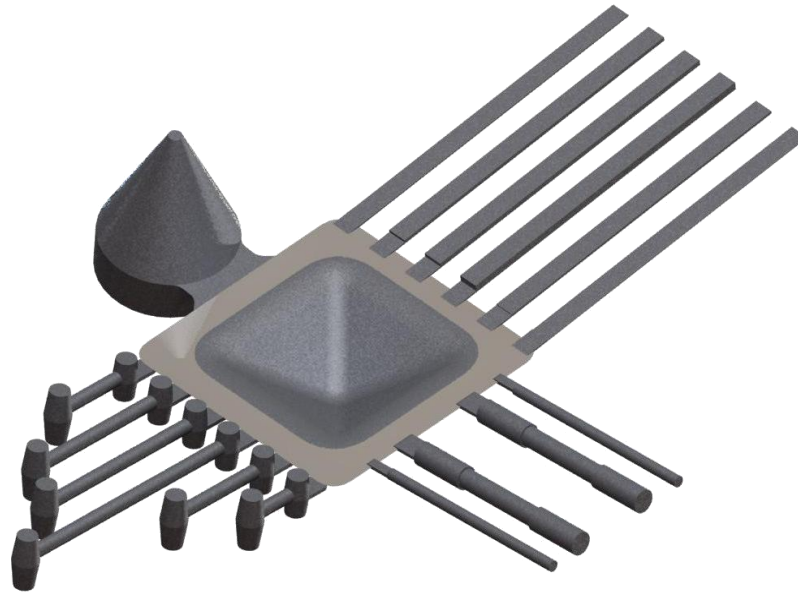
Multifunktionskokille: Virtueller Abguss mit Lage der einzelnen Prüfkokillen für Fließlänge, Zugstäben, Warmrissneigung und Lunckerneigung (Tatur).
